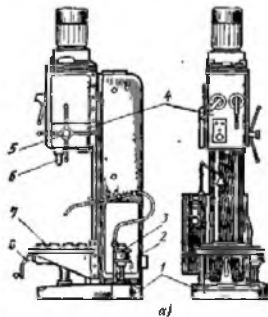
Станок вертикально-сверлильный 2Н118
